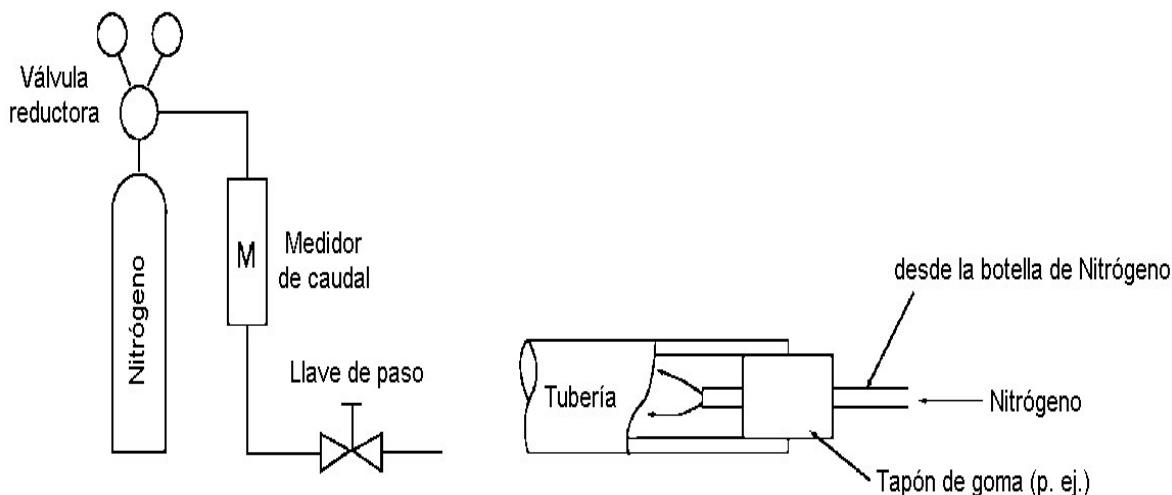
Uso de Nitrógeno para prevenir la formación de óxido durante la soldadura
